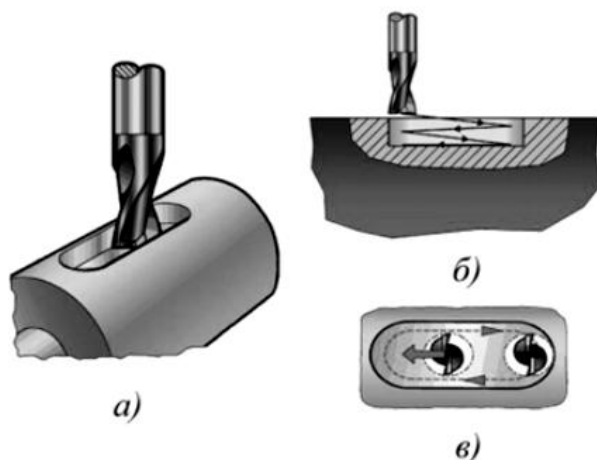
Обработка шпоночных пазов: а – общий вид фрезерования паза; б – схема врезания фрезы; в – схема перемещения фрезы в горизонтальной плоскости паза
